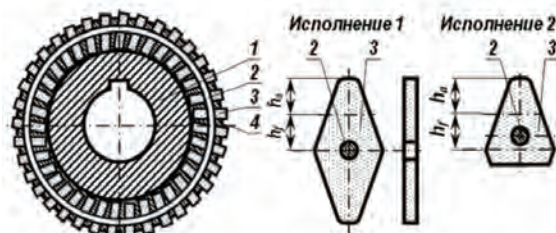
Пружинно - пластинчатая сборная червячная фреза
